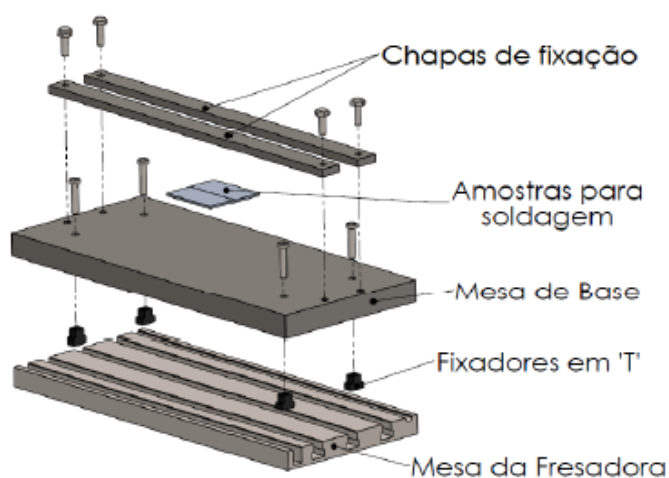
Desenho do Conjunto de Fixação de Chapas
